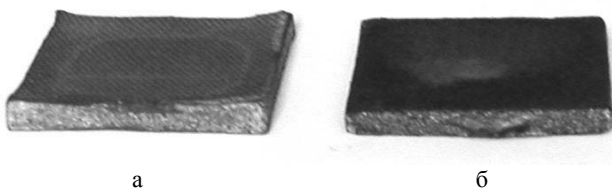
Форма спрессованных заготовок с прямоугольными боковыми ребрами (а) и с фасками на боковых ребрах (б)
